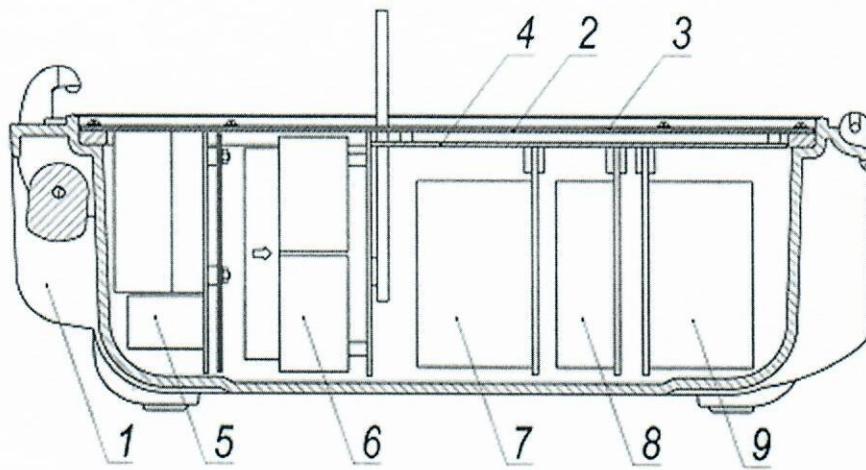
Расположение блоков внутри корпуса КИП-01ВУ.
